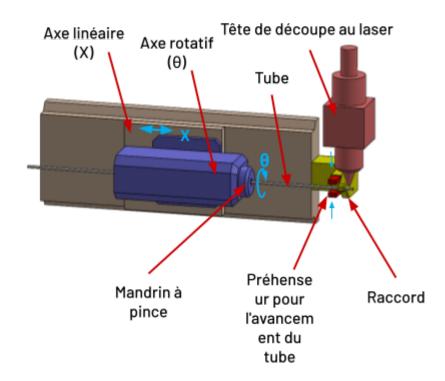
Composants mécaniques d'un système de mouvement de coupe de tubes de précision pour la manipulation de pièces.
